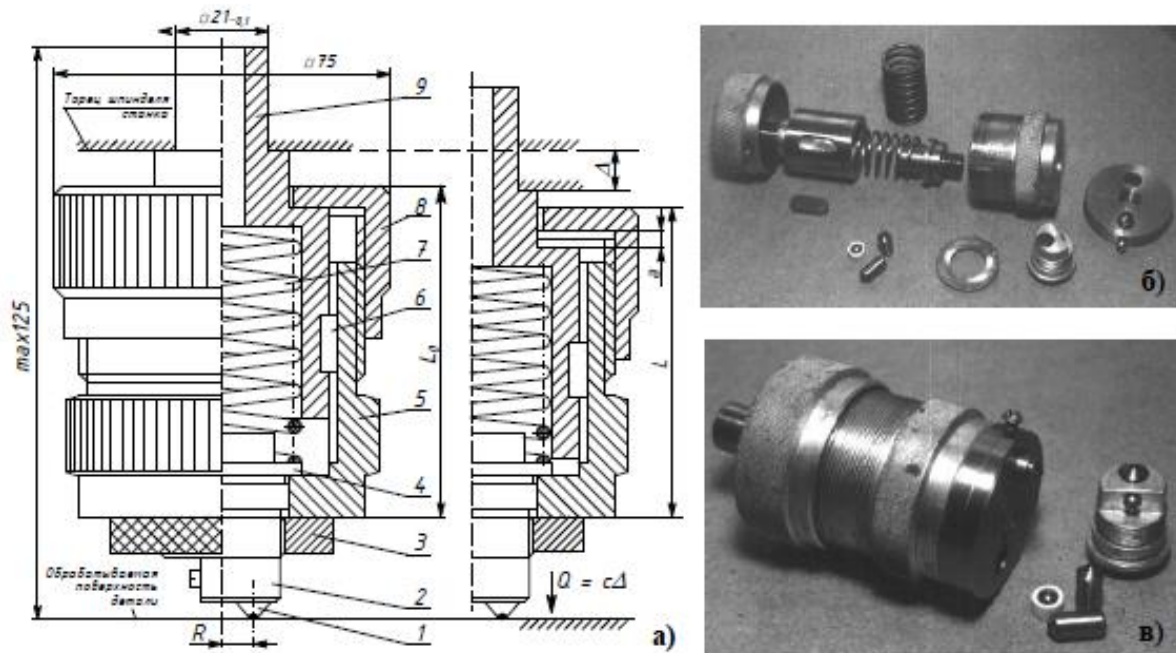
Конструкція інструменту для алмазного вигладжування плоских поверхонь деталей: а – конструкція вигладжувача: 1 – вставка з індентором з АСПК; 2 – тримач; 3 – гайка; 4 – корпус утримувача; 5 – корпус; 6 – шпонка; 7 – пружина; 8 – кришка; 9 – хвостовик; б – вигладжувач у розібраному стані; в – загальний вигляд алмазного вигладжувача з різними власниками та інденторами
